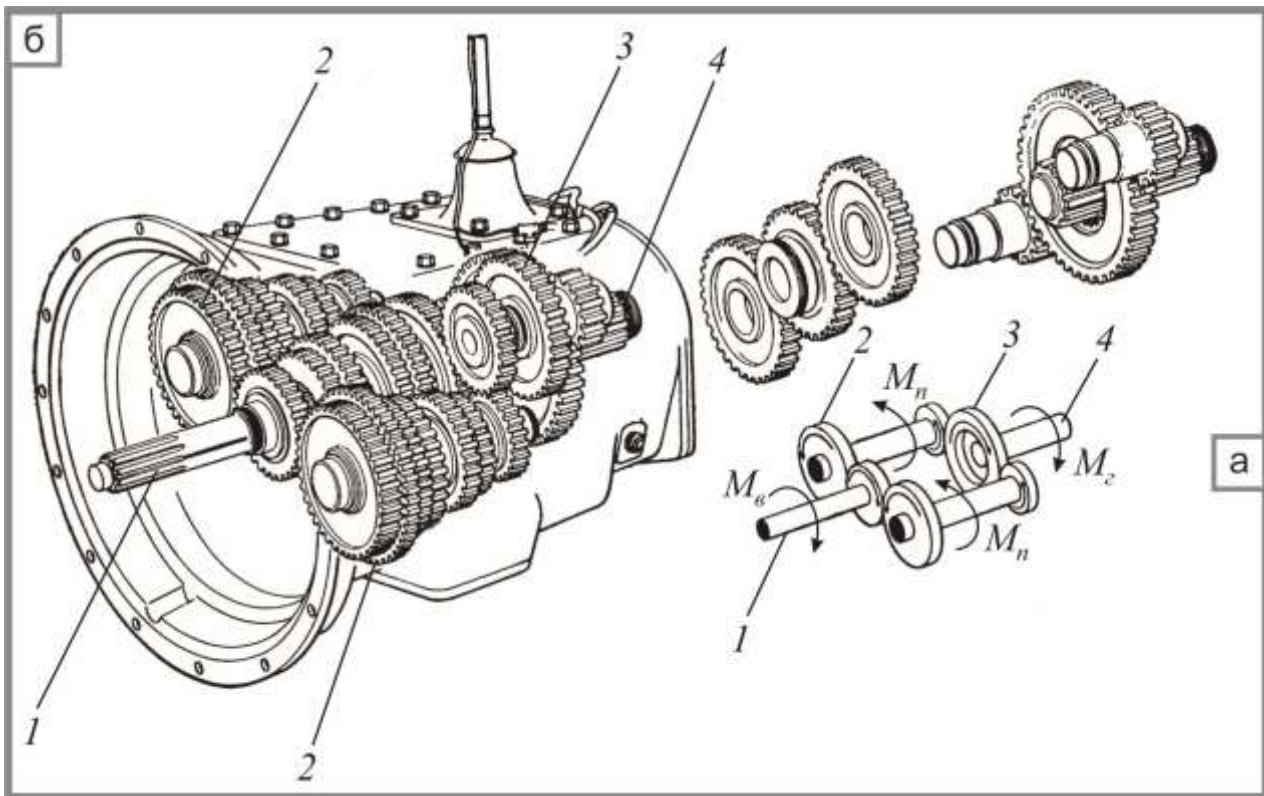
Схема розподілення крутного моменту  $M_e$  (а) вхідного валу і компонування десятиступінчастої коробки передач EATON Fuller тип RT-910 з двома паралельними проміжними валами (б): 1 – вхідний вал з ведучою шестернею; 2 – шестерні проміжних валів; 3 – шестерня головного валу; 4 – головний вал
